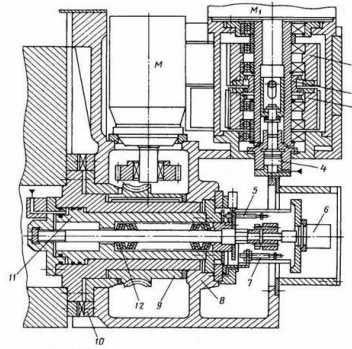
Фрагмент конструкции револьверной головки карусельно-шлифовального станка
